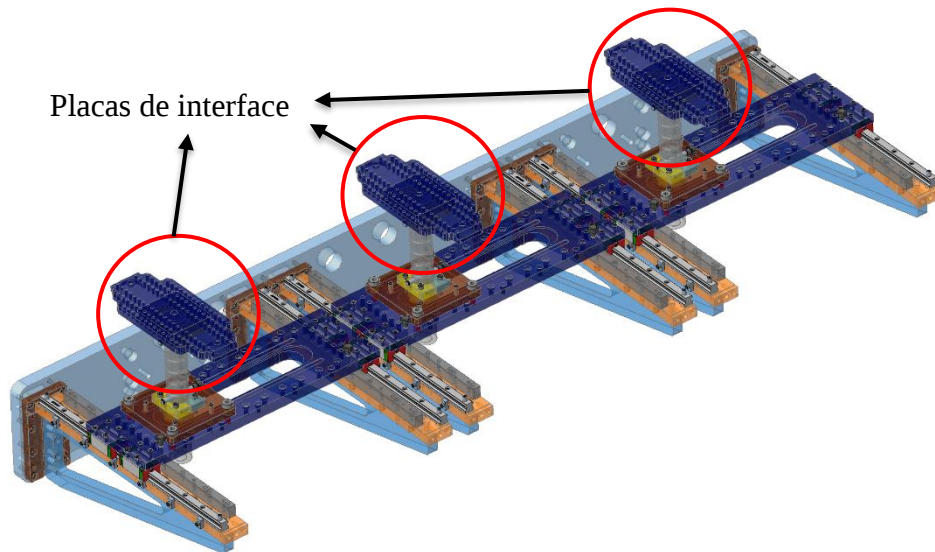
Jig standard utilizado no corte a laser, e placa de interface
